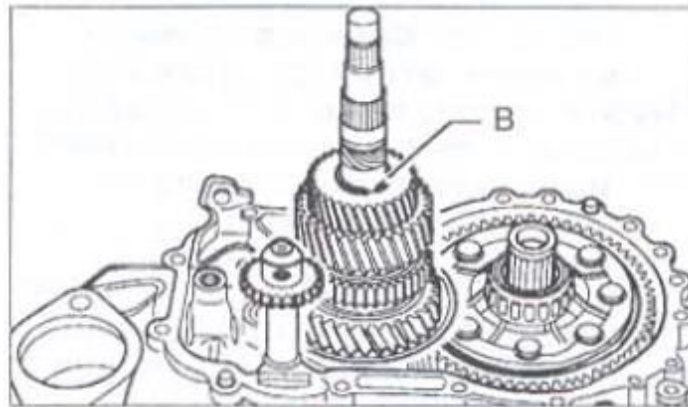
Розташування стопорного кільця шестерні третьої передачі
